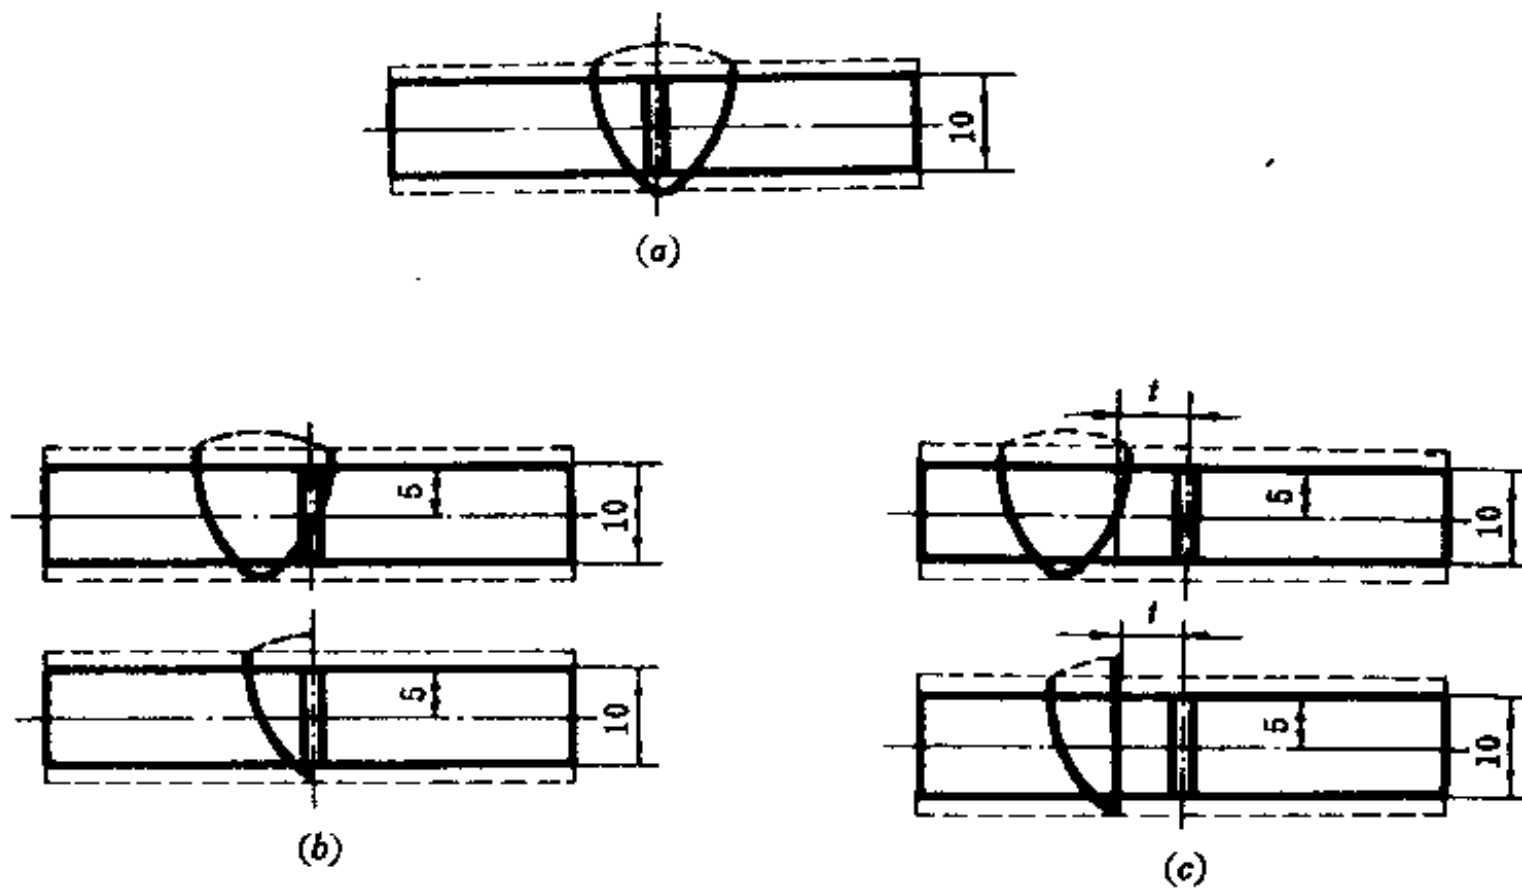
焊缝、熔合线和热影响区的缺口位置
